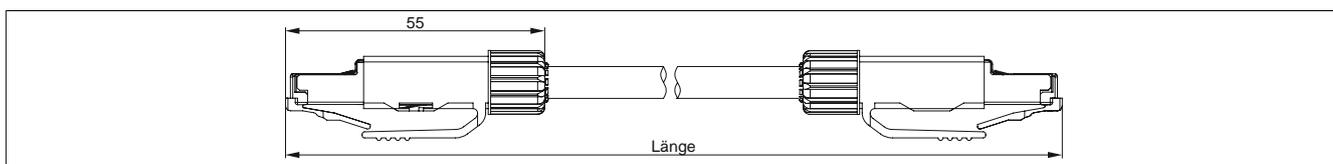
5CASD3.xxxx-00 - Abmessungen
